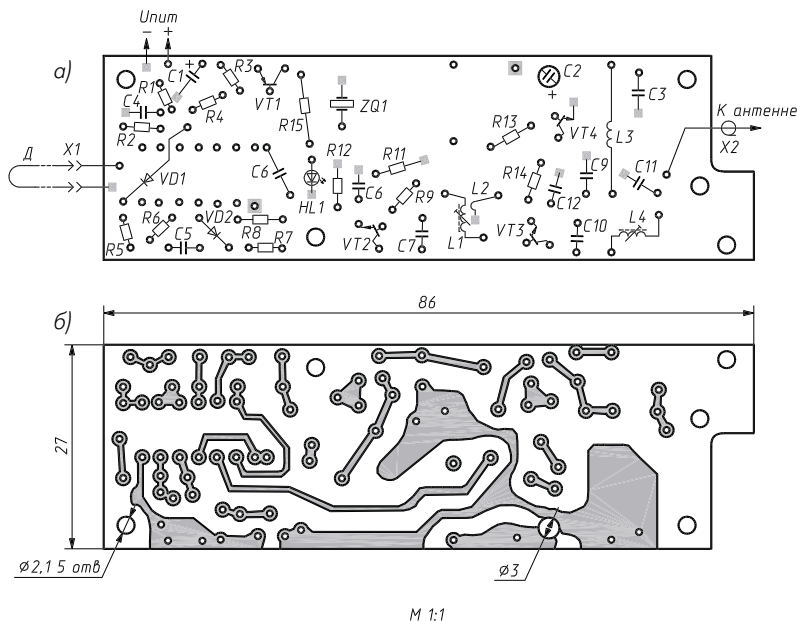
Монтажная схема охранной системы и печатная плата
